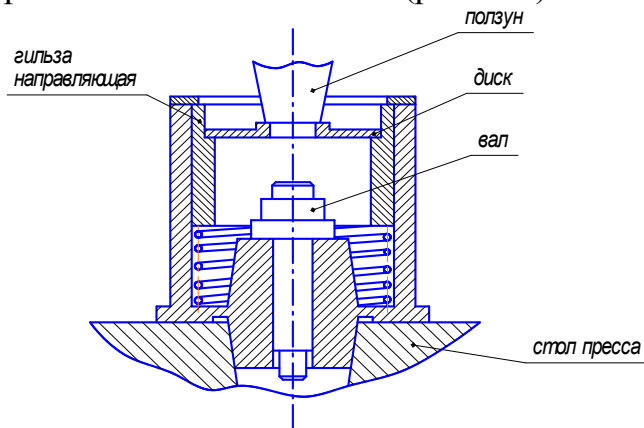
Схема приспособления для запрессовки тонких дисков на вал
